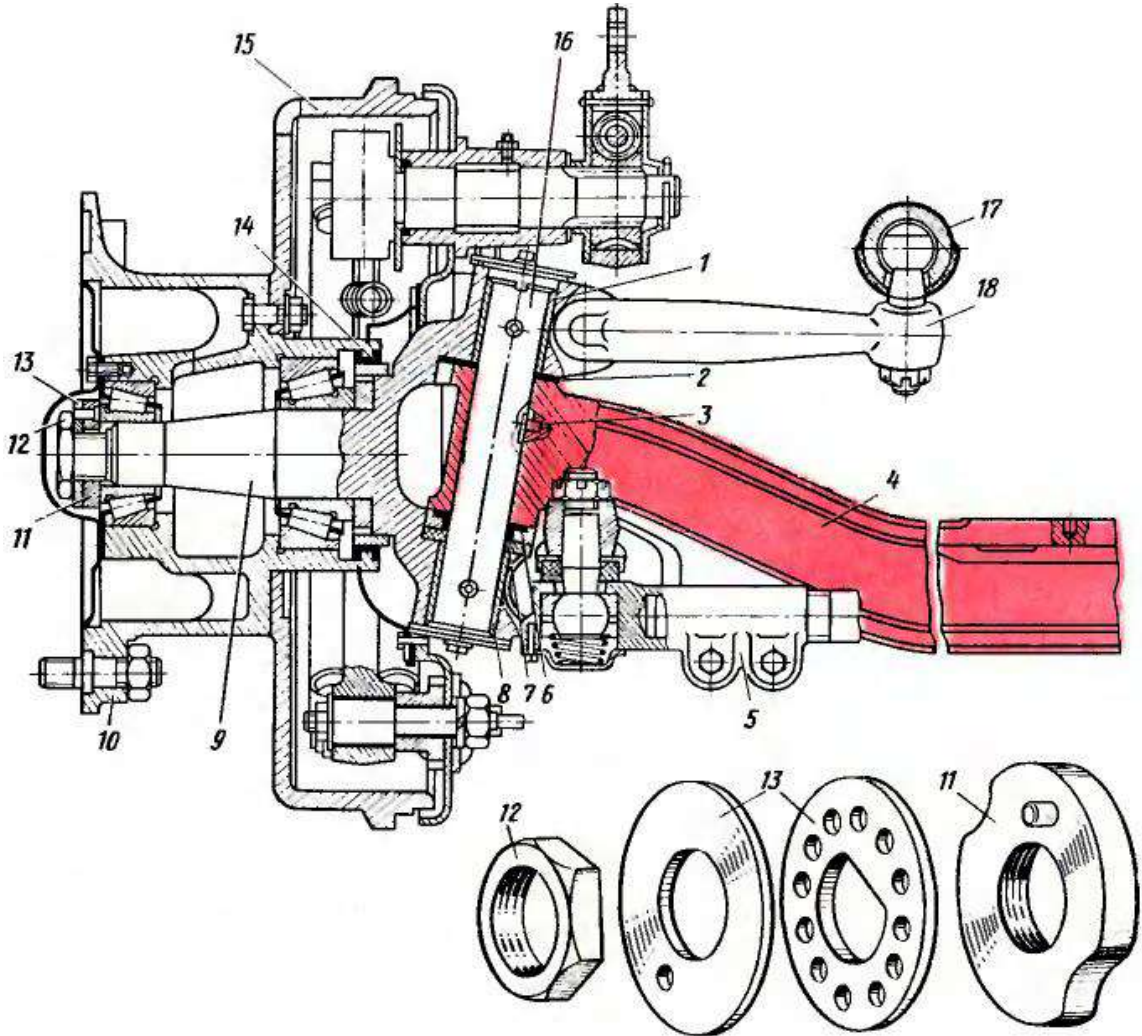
Передній міст вантажного автомобіля ЗІЛ-130: 1 та 8 – втулки шворня; 2 – регулювальні прокладки; 3 – клиновий болт; 4 – балка мосту; 5 – поперечна рульова тяга; 6 та 7 – шайби опорного підшипника; 9 – поворотна цапфа; 10 - маточина колеса; 11 – регулювальна гайка; 12 – контргайка; 13 – замкова шайба; 14 – сальник; 15 - гальмівний барабан; 16 – шворень; 17 - поздовжня рульова тяга; 18 – поворотний важіль
